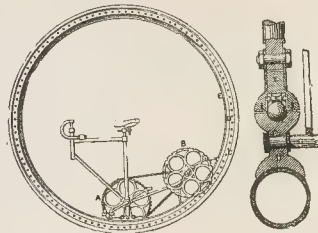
CORTE Y DETALLES DEL MECANISMO.
